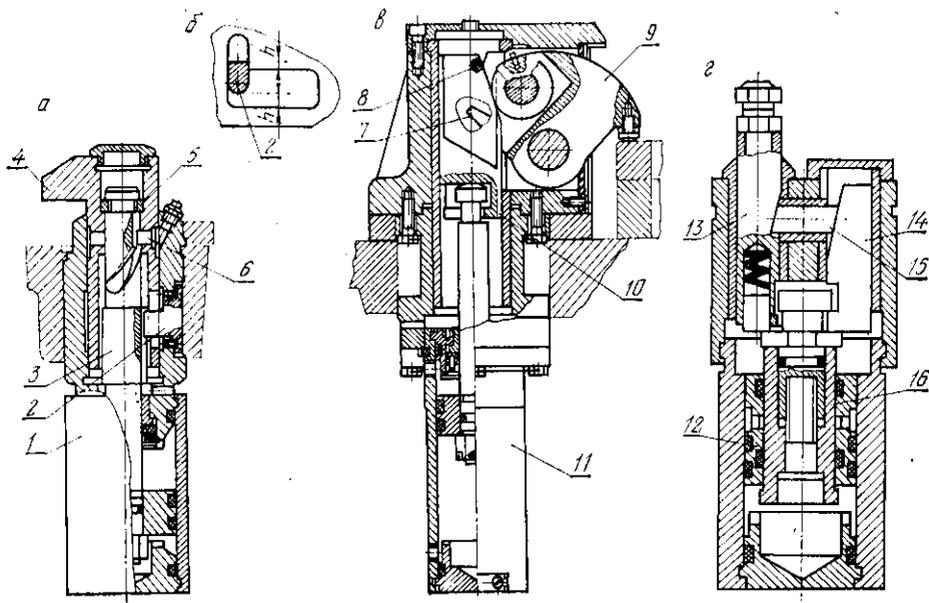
Унифицированные узлы приспособлений агрегатных станков:
